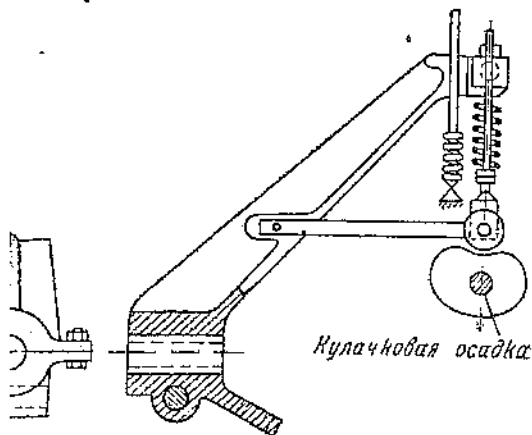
Сварочная машина АТА-40-8 с радиальным перемещением верхнего электрода.
